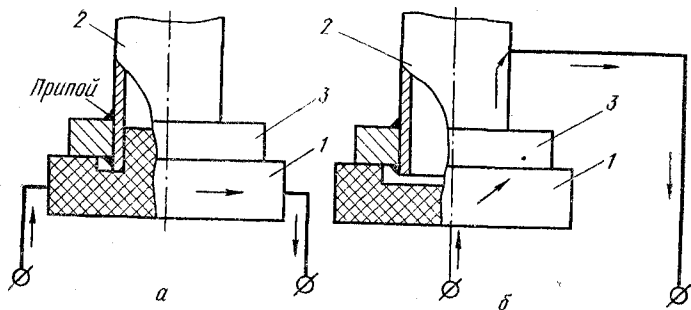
Схемы установок для пайки с электроконтактным нагревом
